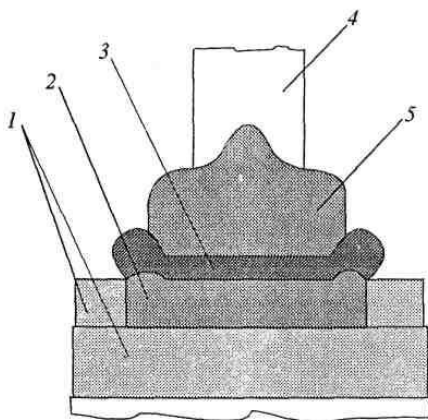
Схема монтажа алюминиевой проволоки к контактной площадке на кристалле: 1 – диэлектрическая пленка; 2 – легированный алюминий; 3 – чистый алюминий; 4 – алюминиевая проволока; 5 – сварное соединение
